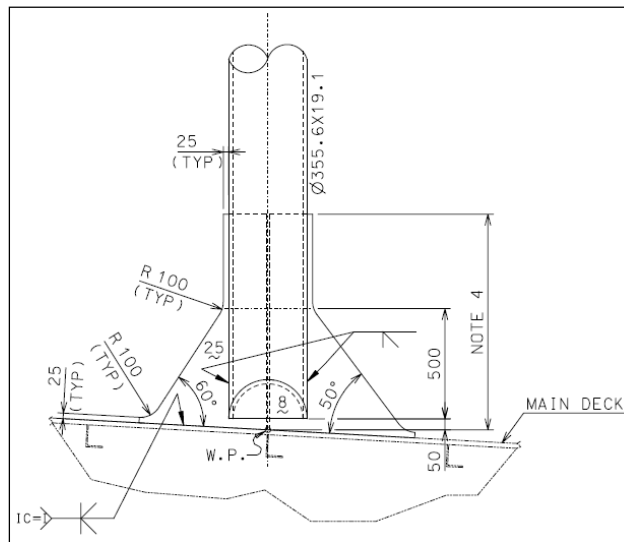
Suporte do módulo – conexão tipo 3 – vista transversal.
